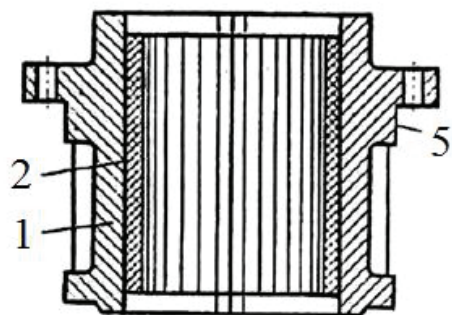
Направляющий подшипник с лигнофолиевыми вкладышами:
